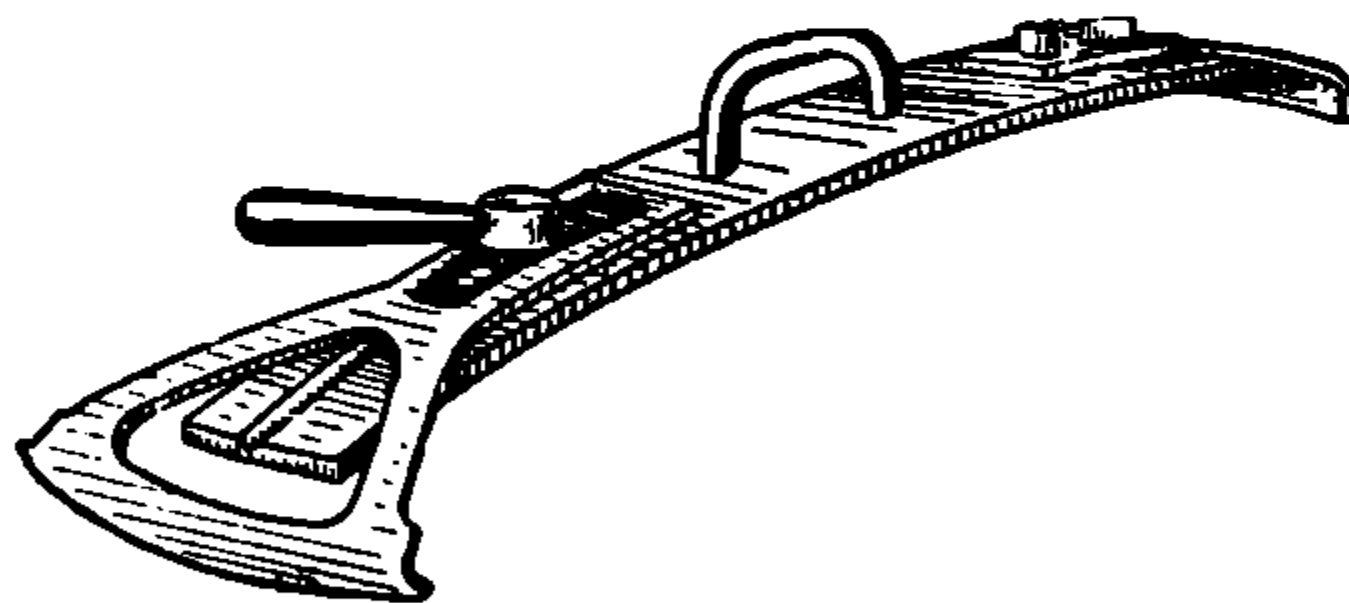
Пневматический подъемник с шарнирным захватом для подачи бандажей в бандажный горн:
